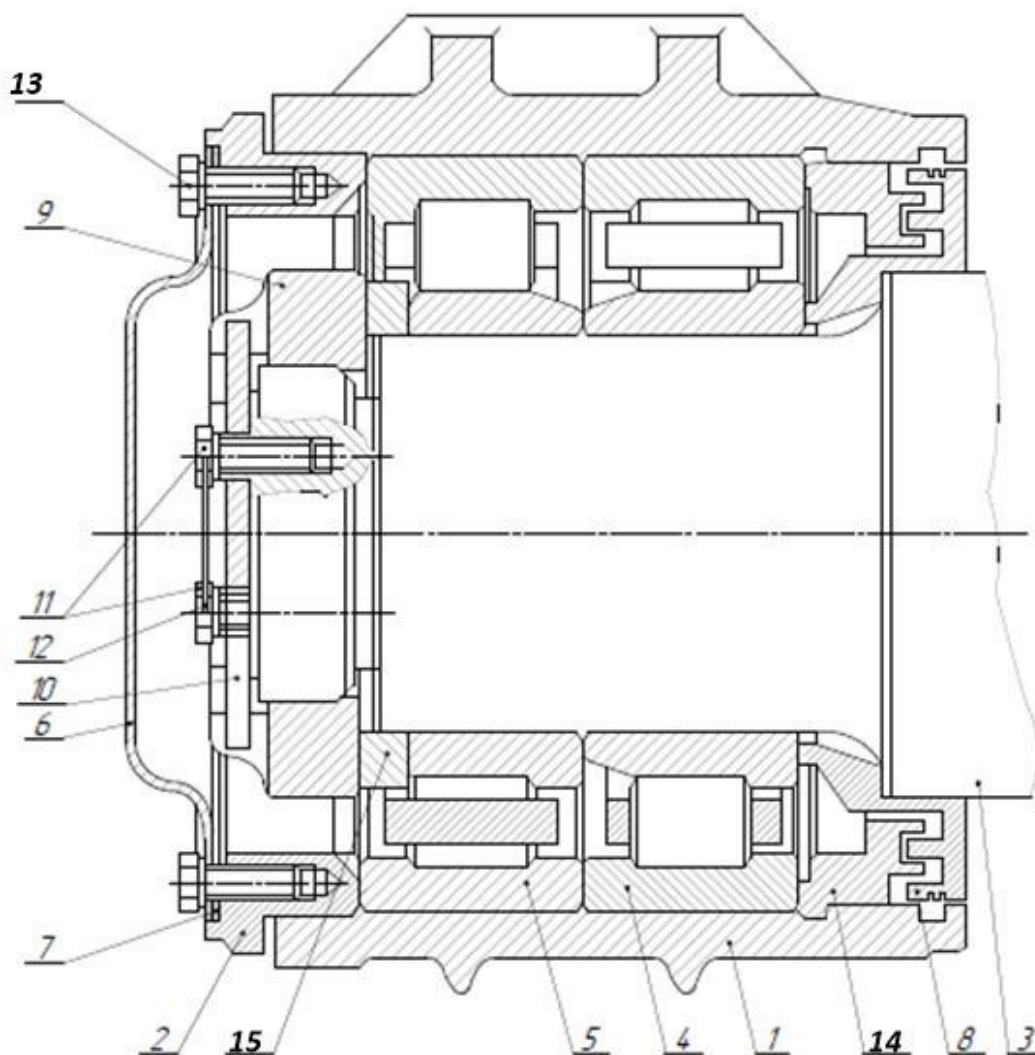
Буксовый узел с двумя роликовыми цилиндрическими подшипниками с торцевым креплением гайкой М110:
